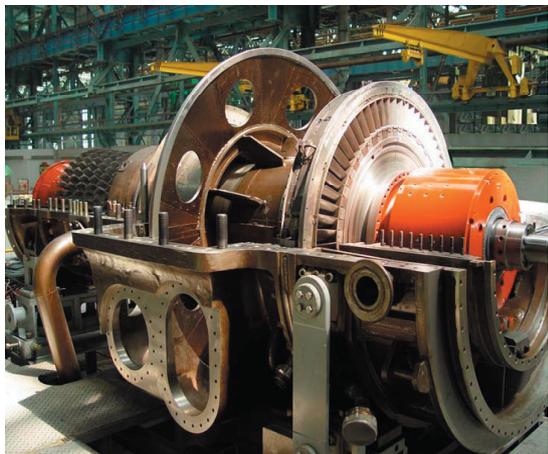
Газотурбинный двигатель ГТ-009М (верхняя крышка снята; на переднем плане радиальный магнитный подшипник)
